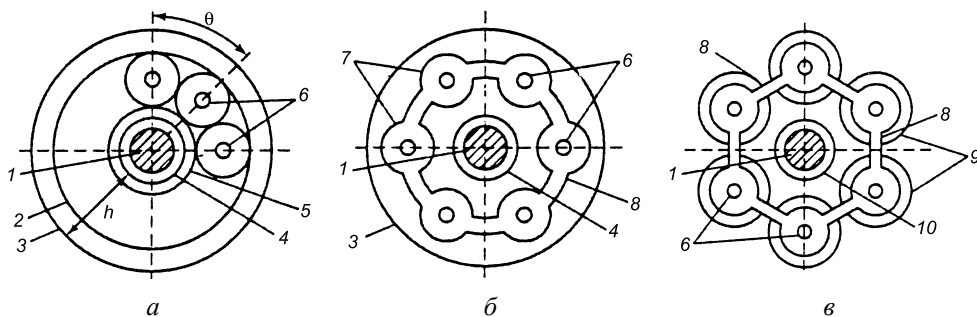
Схемы конструкций встроенных КС ГТУ (вид со стороны компрессора) [15]: *а* – кольцевая; *б* – трубчато-кольцевая; *в* – секционная; 1 – вал ротора ГТУ; 2 – наружная обечайка кольцевой пламенной трубы; 3 – наружный (кольцевой) корпус камеры сгорания; 4 – внутренний корпус; 5 – внутренняя обечайка кольцевой пламенной трубы; 6 – форсунок; 7 – отдельные пламенные трубы; 8 – патрубок для переброски пламени; 9 – корпус; 10 – кожух вала.
